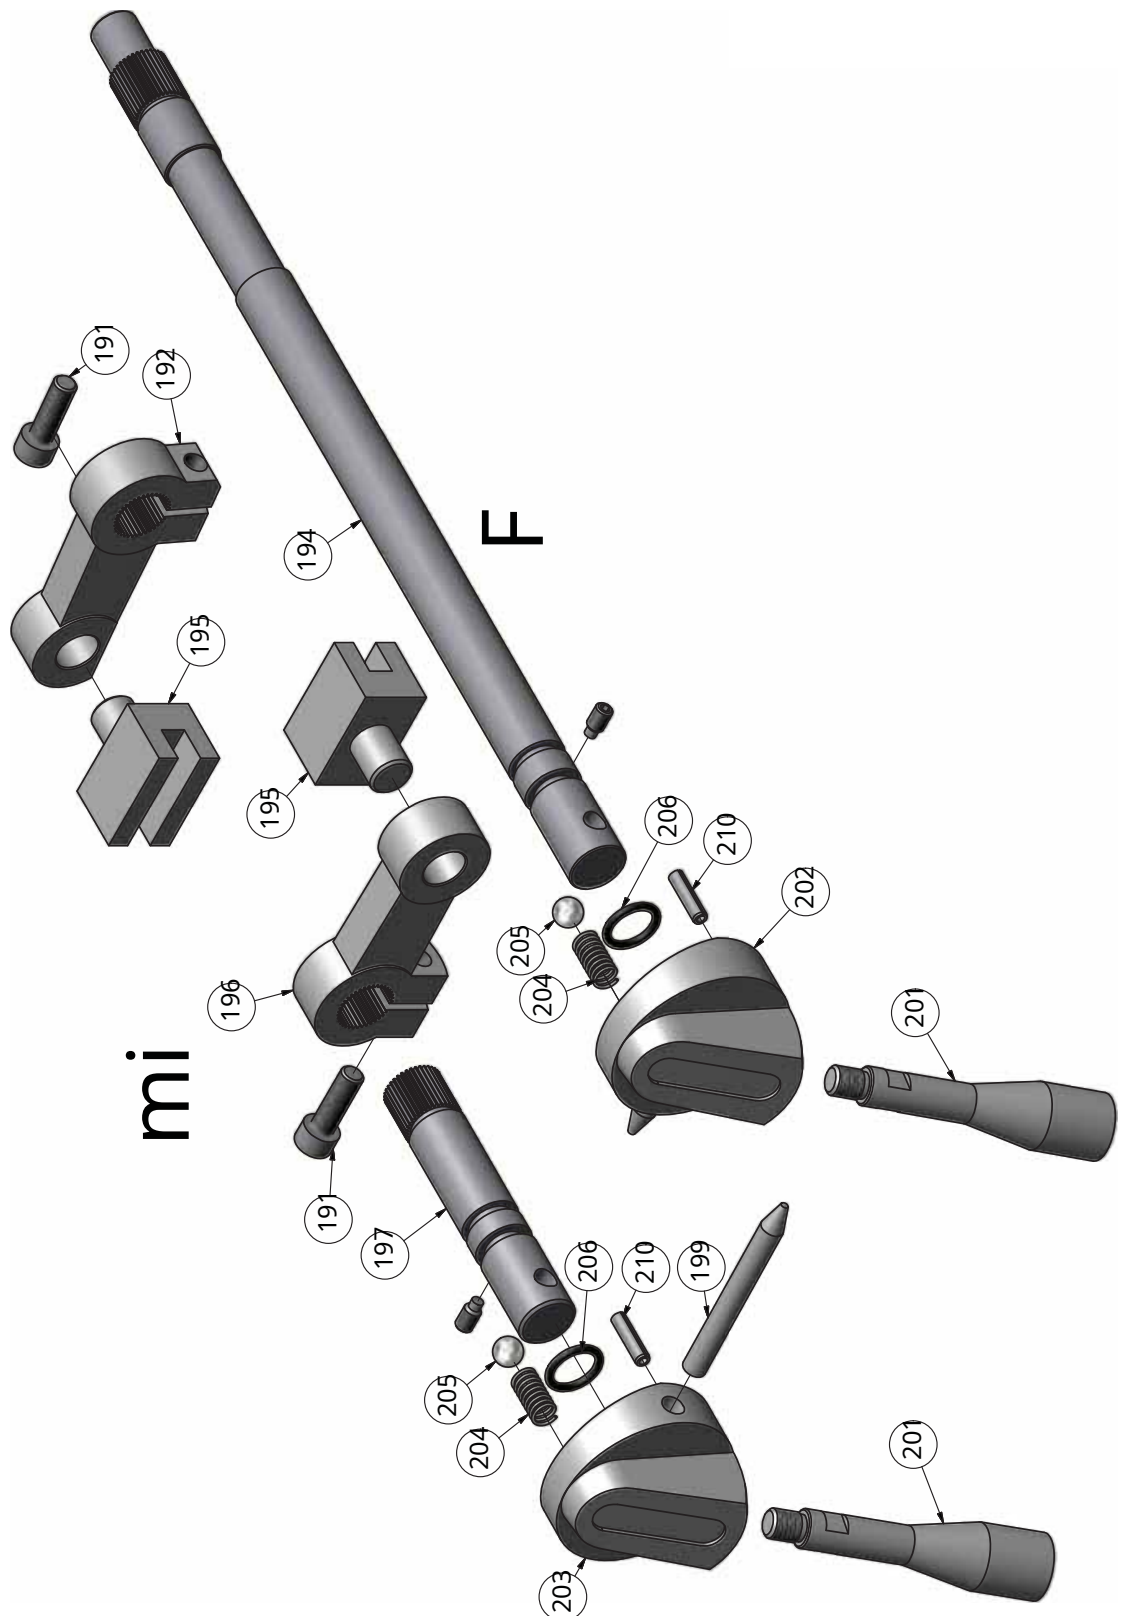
Getriebe Bohrspindel 3 de 4 - Husillo principal de caja de cambios 3 de 4
